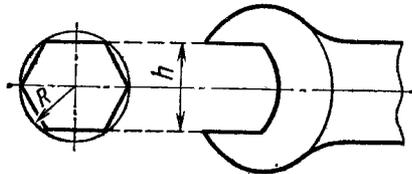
Пример разметки шестиугольника под размер зева гаечного ключа
